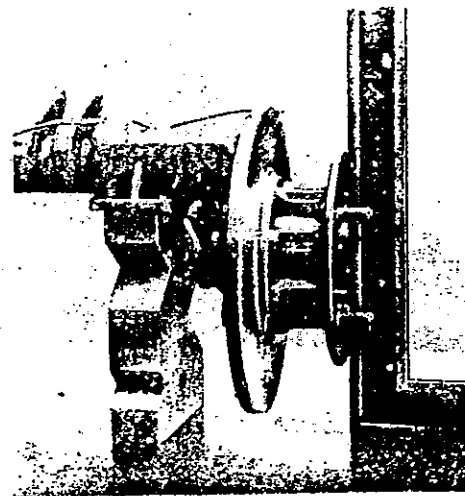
/4 - Contrôle position d'équerre de l'essieu sur plan vertical.
